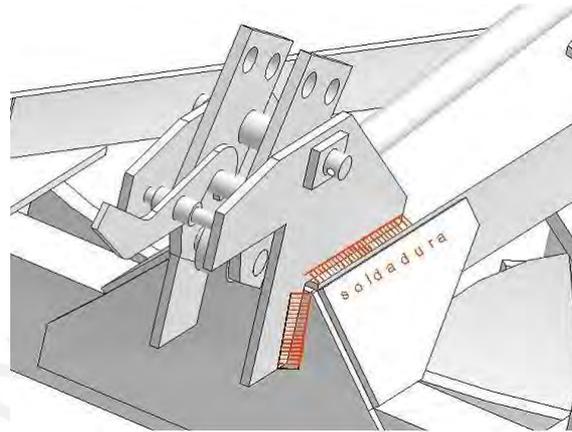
Cordones de soldadura en los soportes del enganche superior de 3 ptos.
